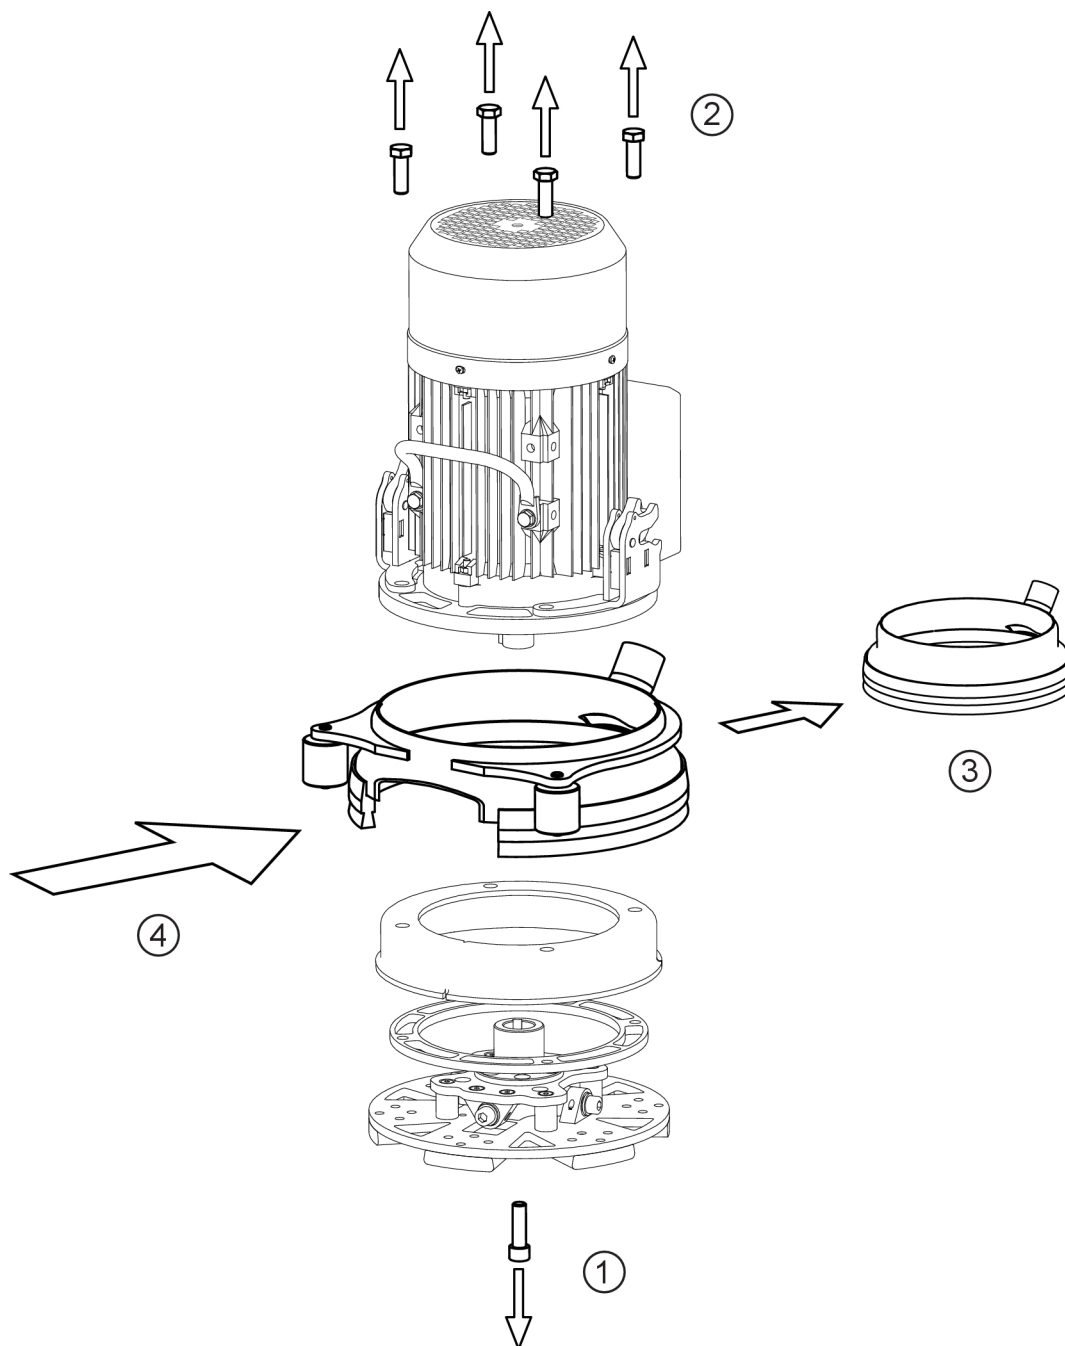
Снятие крышки и установка крышки для шлифовки кромок.
